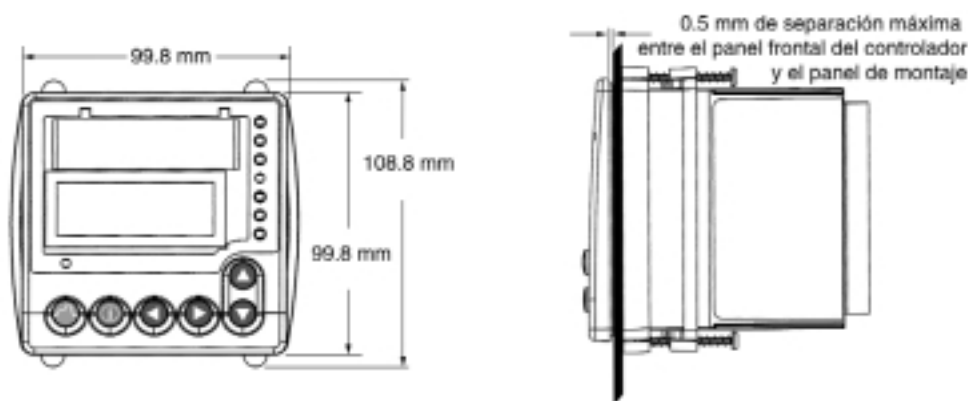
Dimensiones de la vista frontal y dimensión de la separación para la junta.
